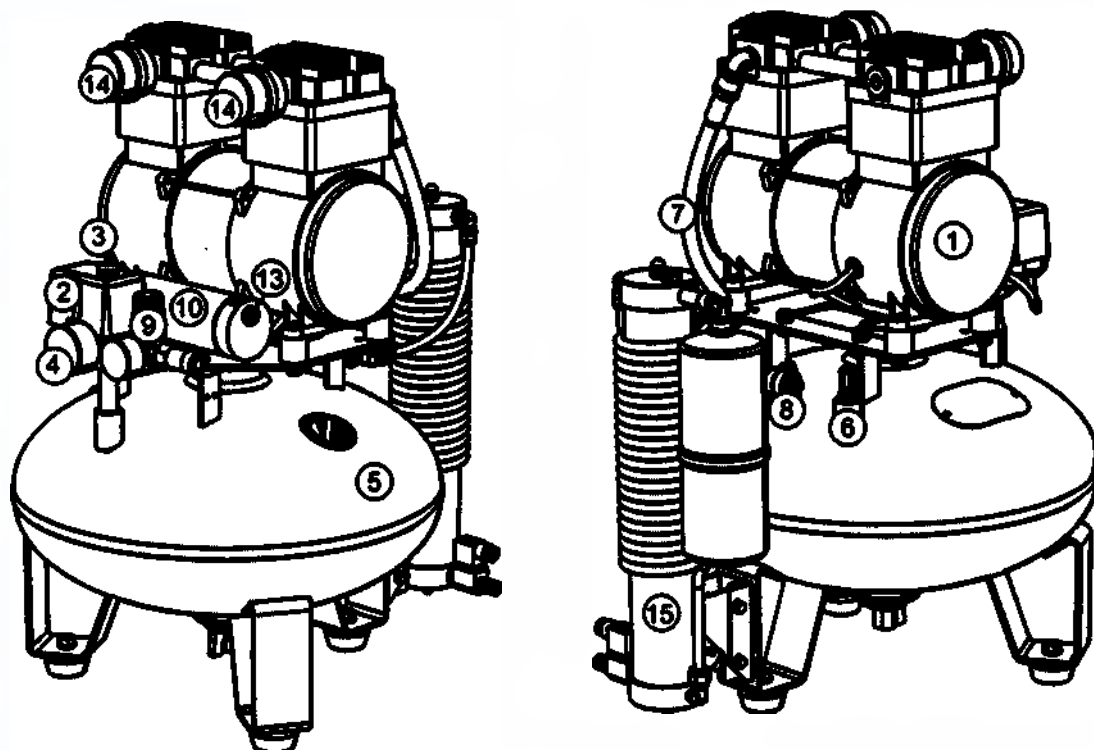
Общий вид компрессора KM-24.OLD15Д,
